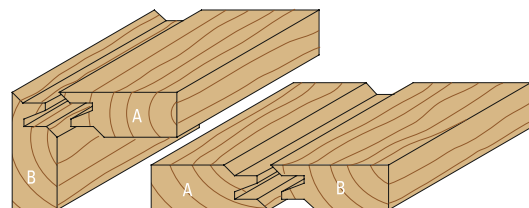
Eckverbindung 90° (links) und plane Verbindung 180° (rechts)
